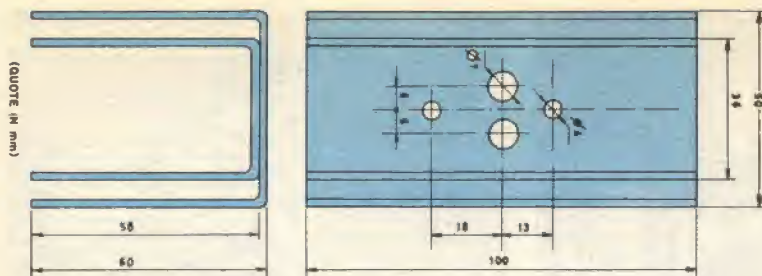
Disegno costruttivo e montaggio relativo al dissipatore di calore.
